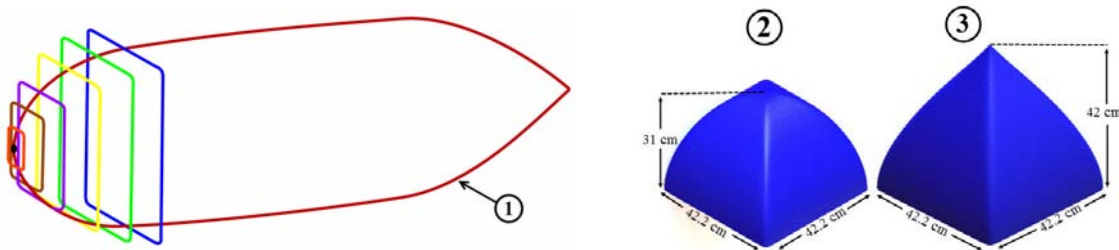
1) Vista a detalle del ensamblaje de las figuras de la ecuación de la elipse y el perfil modificado, 2) parte frontal, 3) parte trasera, estas últimas dos secciones elaboradas en SolidWorks.
